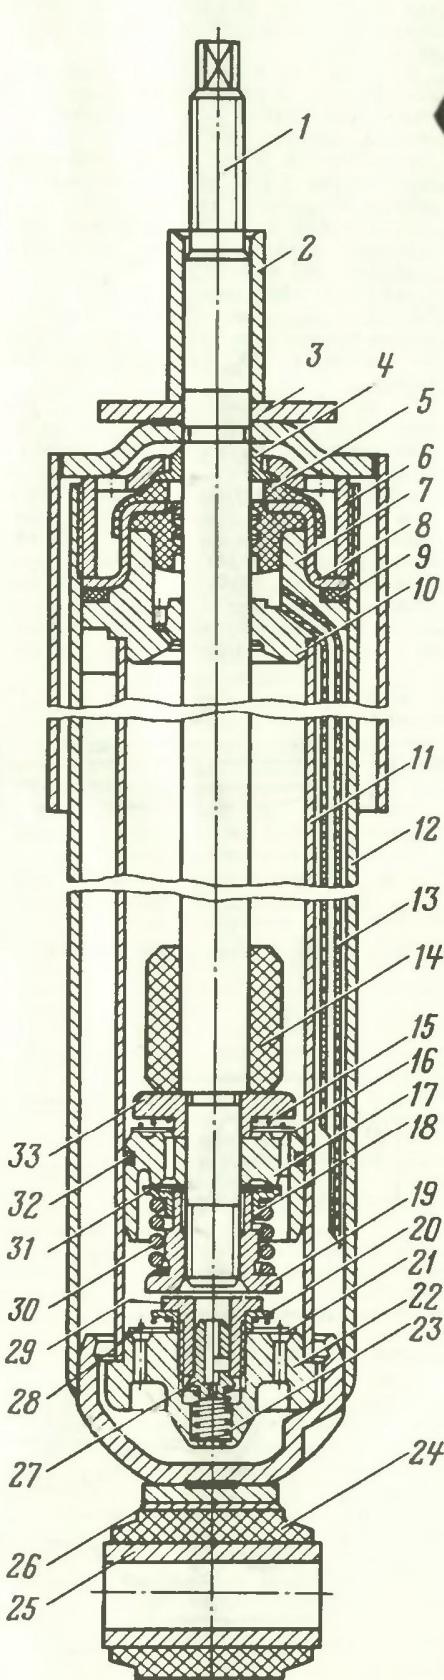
Конструкция амортизатора «жигулей»: 1 — шток; 2 — втулка верхнего шарнира; 3 — крышка с конжуком сборке; 4 — защитное кольцо; 5 — прокладка; 6 — гайка резервуара; 7 — сальник штока; 8 — обойма сальника; 9 — уплотнительное кольцо; 10 — направляющая втулка; 11 — цилиндр; 12 — резервуар с проушиной сборке; 13 — сливная трубка; 14 — буфер хода отбоя; 15 — пружина перепускного клапана; 16 — тарелка перепускного клапана; 17 — поршень; 18 — тарелка клапана отбоя; 19 — гайка клапана отбоя; 20 — ограничительная тарелка впускного клапана; 21 — тарелка впускного клапана; 22 — корпус впускного клапана; 23 — пружина клапана сжатия; 24 — резиновая втулка шарнира; 25 — внутренняя втулка шарнира; 26 — наружная втулка шарнира; 27 — втулка клапана сжатия; 28 — пружина впускного клапана; 29 — гайка клапана сжатия; 30 — пружина клапана отбоя; 31 — пакет дисков; 32 — поршневое кольцо; 33 — ограничительная тарелка.
